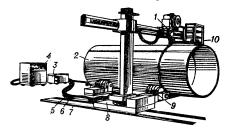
Установка для дуговой автоматической сварки: 1— сварочный аппарат; 2— свариваемое изделие; 3— шкаф с аппаратурой управления; 4— источник с аппаратуров управления, 4 — источик тока; 5 — провода управления; 6 — токопровод; 7 — рельсовый путь; 8 — тележка с колонной; 9 — роликовый стенд; 10 — площадка обслуживания.
